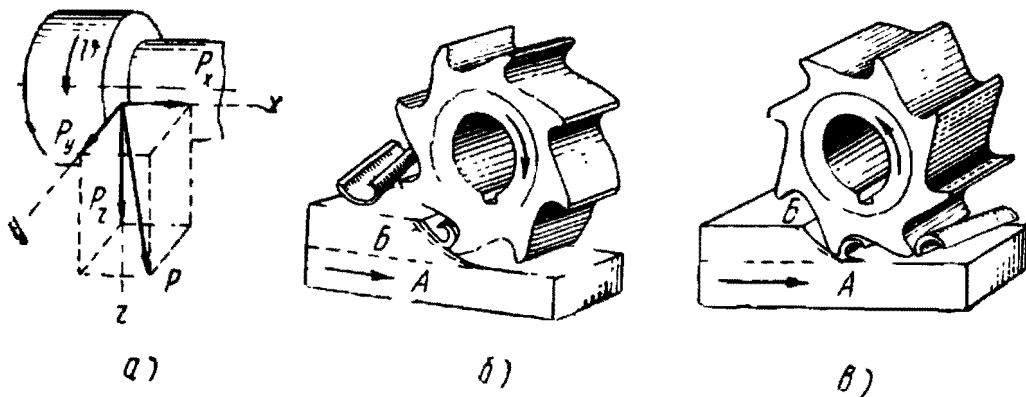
Схема сил резания (а) при токарной обработке, фрезерование против подачи (б) и попутное фрезерование (в)
